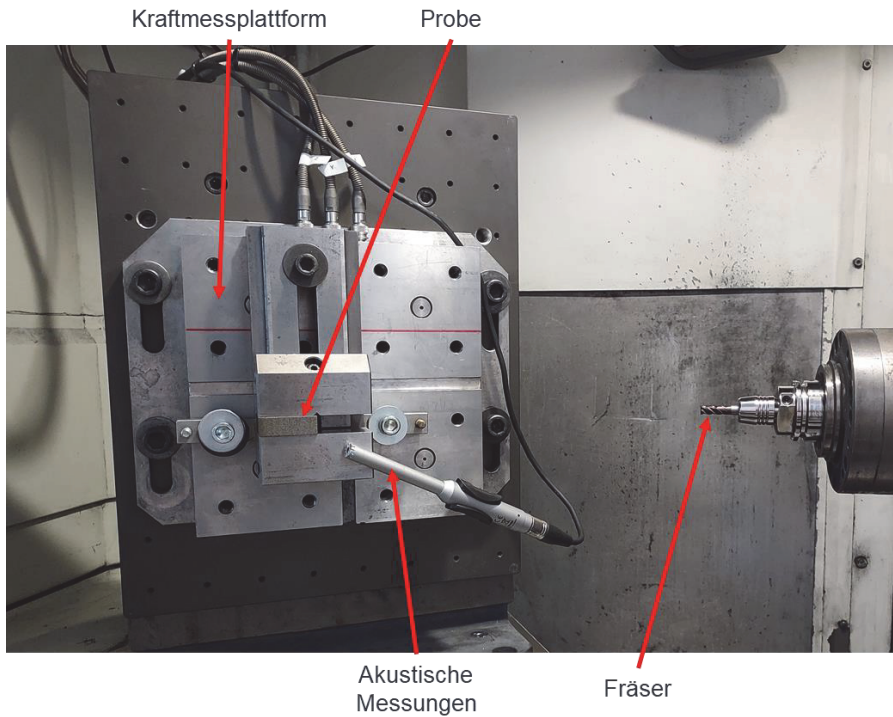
Versuchsaufbau zum Fräsen der Verzugsproben auf einer Heller MC16
